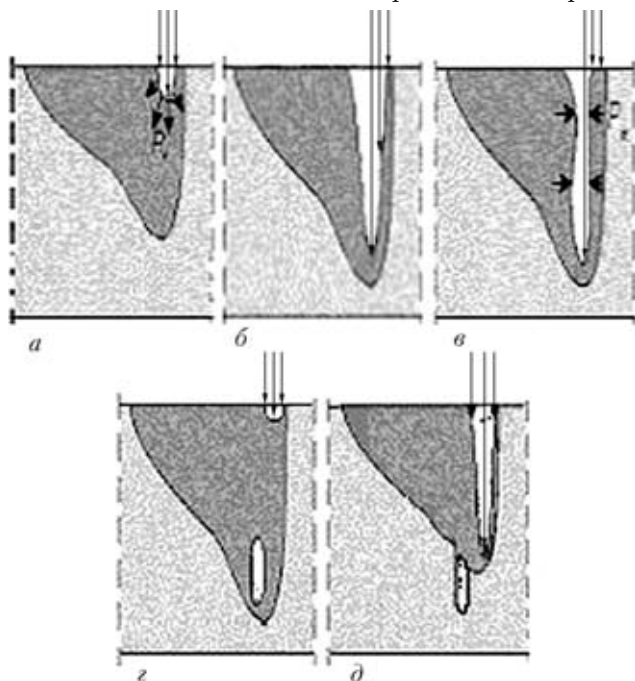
Стадии формирования парогазового канала при лучевых способах сварки
